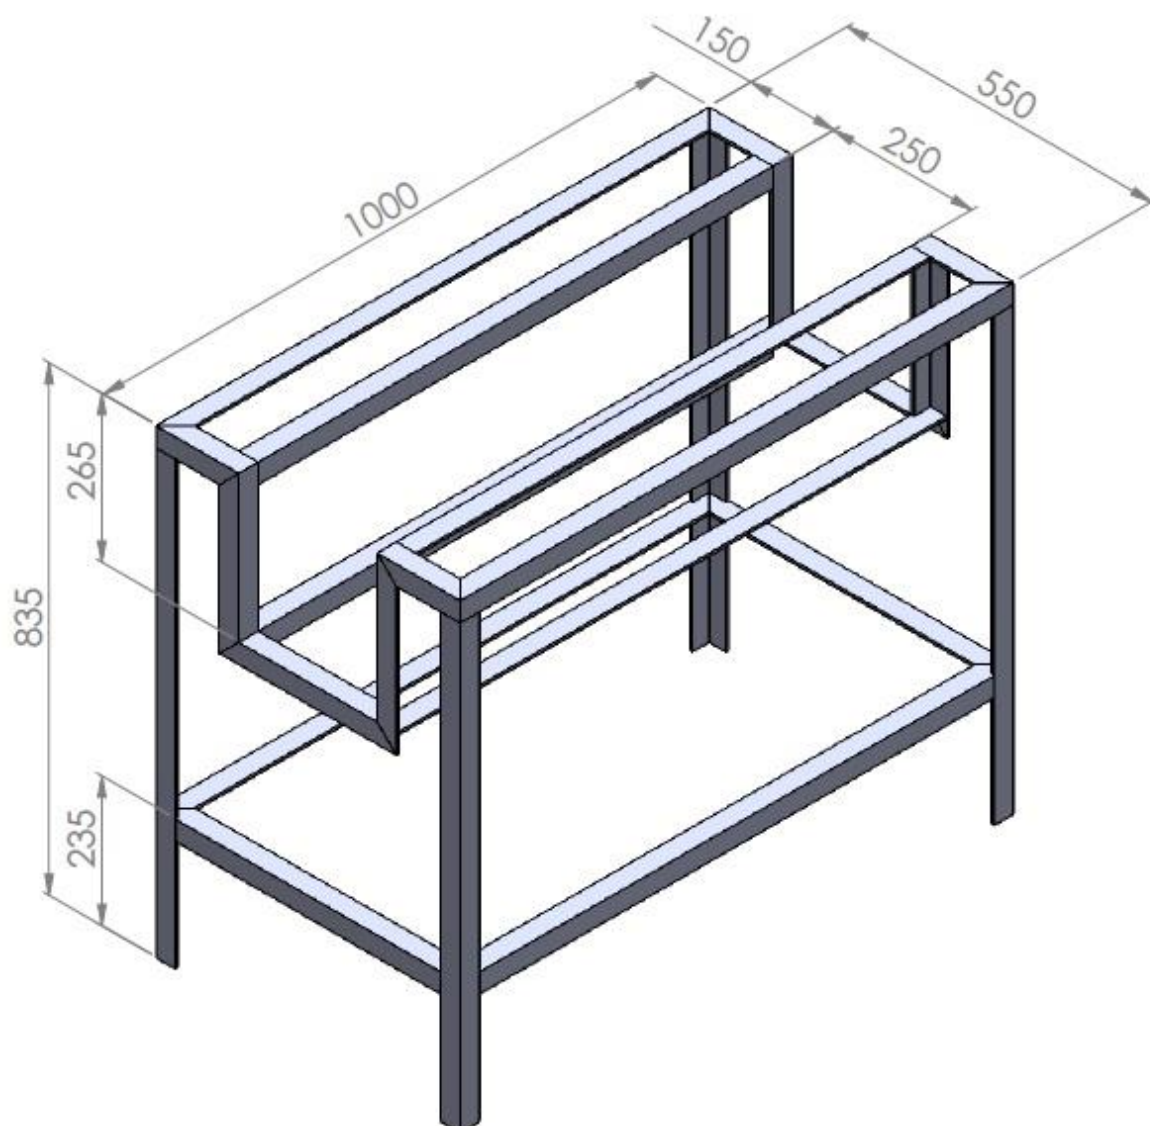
Modelo dimensionado da estrutura do dispositivo de corte
